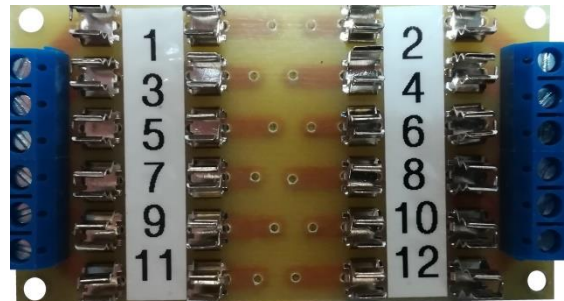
Desenho Final da Placa de Circuito Impresso
